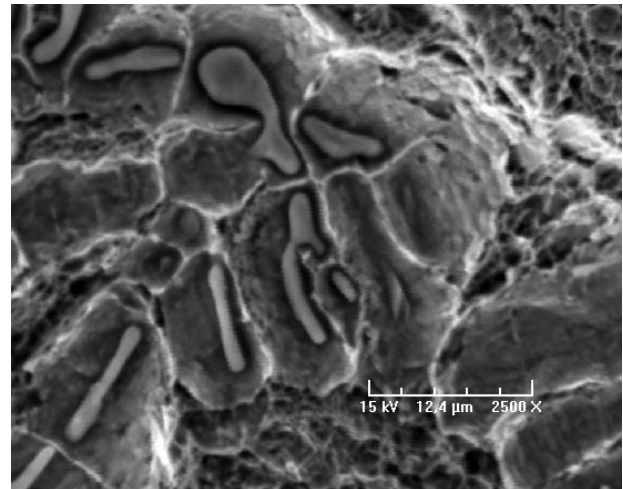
Faciès de rupture, premiers essais au lanthane, grossissement x2500
